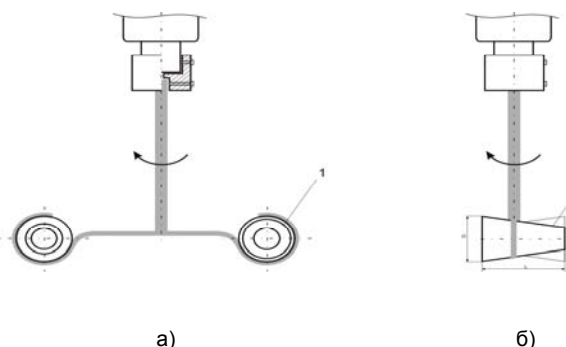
Смеситель: а – вид спереди; б – вид сбоку; 1 – рабочий орган смесителя
